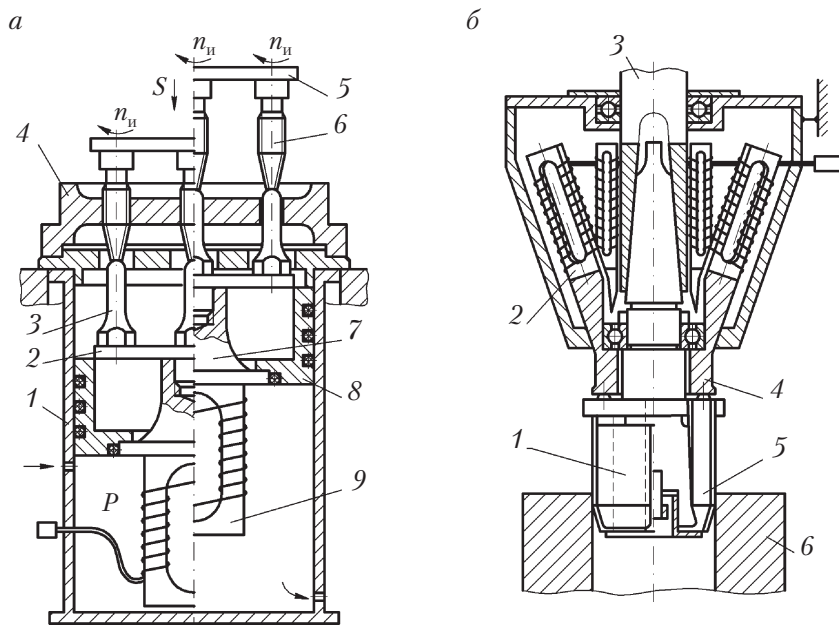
Устройства для ультразвукового раскатывания резьбы малого (*а*) и большого (*б*) диаметров
